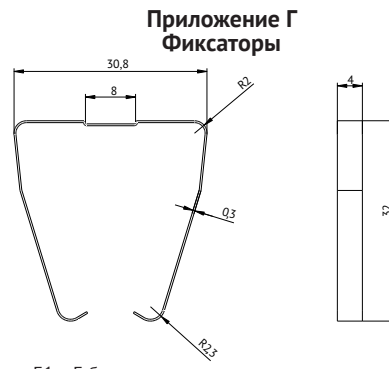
Габаритные, установочные присоединительные размеры фиксатора реле OptiRel 55-H1
